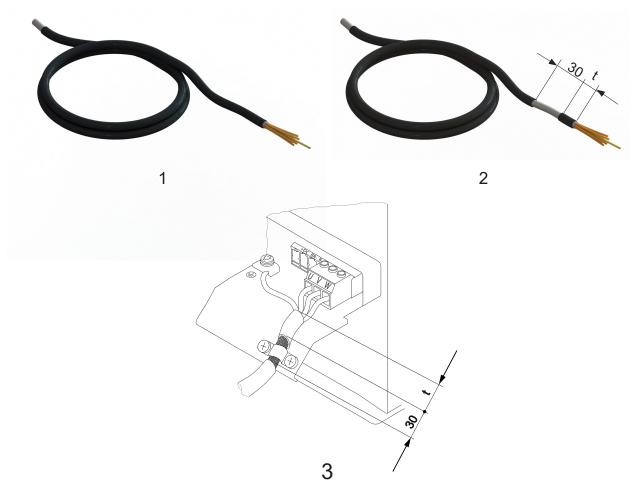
Collegamento del cavo EMC nell'armadio ci comando
